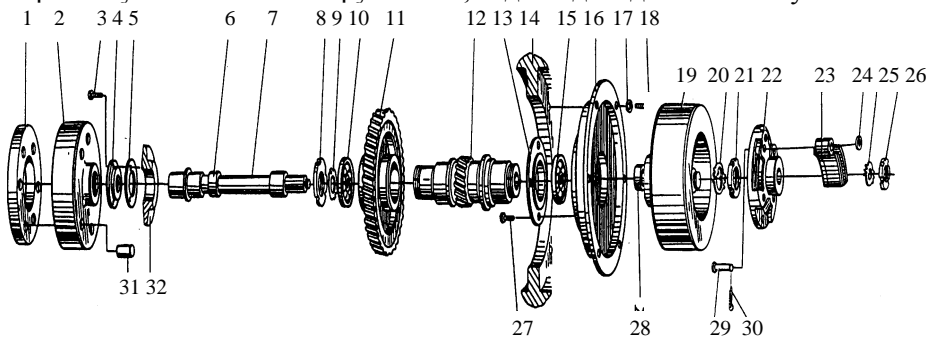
Деталі і вузли приводу сепаратора марки ОСН-С: 1 – гумовий диск; 2 – ведома напівмуфта; 3, 18, 27 – гвинти; 4 – кришка; 5 – прокладка; 6 – бронзова втулка; 7 – суцільний вал; 8, 13 – кришки підшипника; 9 – ущільнення; 10, 15, 28 – підшипники; 11 – зубчасте колесо; 12 – порожнистий вал; 14 – станина; 16 – картерна перегородка; 17, 20, 24, 25 – шайби; 19 – бандаж; 21, 26 – гайки; 22 – ведучий диск; 23 – колодка; 29, 31 – палець; 30 – шплінт; 32 – корпус
